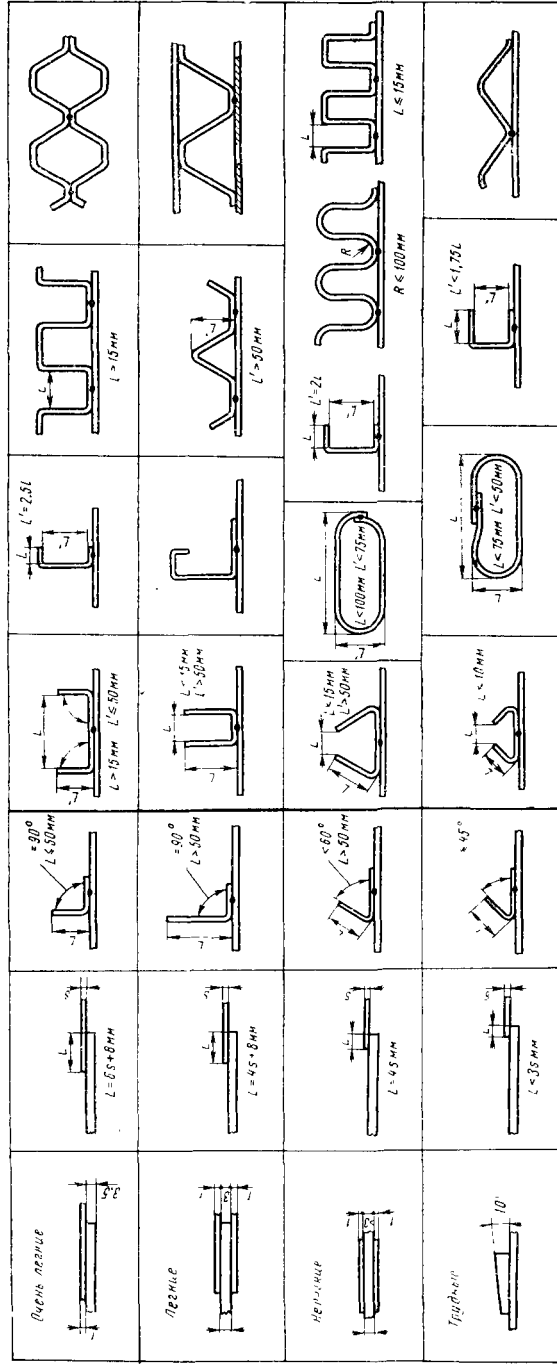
Примеры соединений при точечной сварке:
